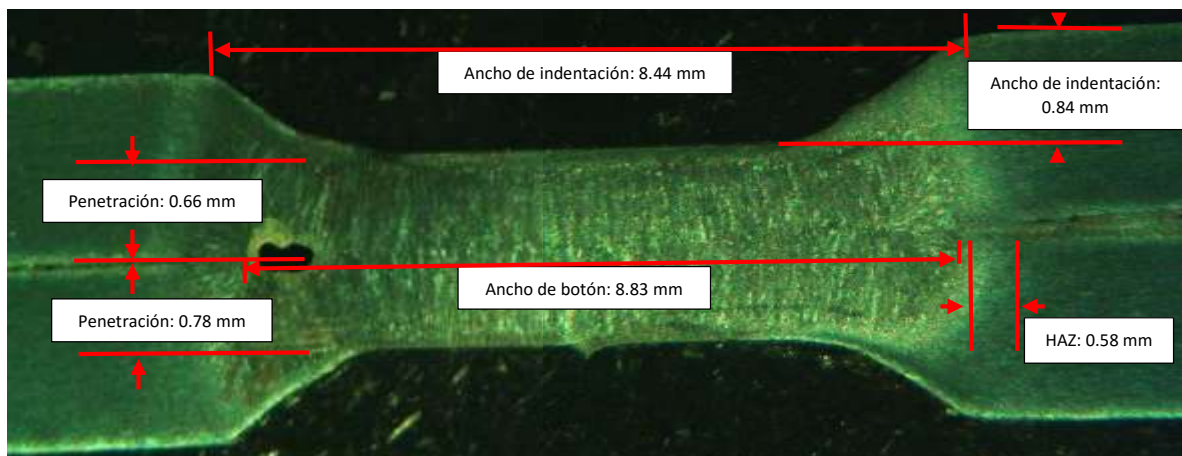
Mediciones realizadas en el botón de soldadura número 4.
